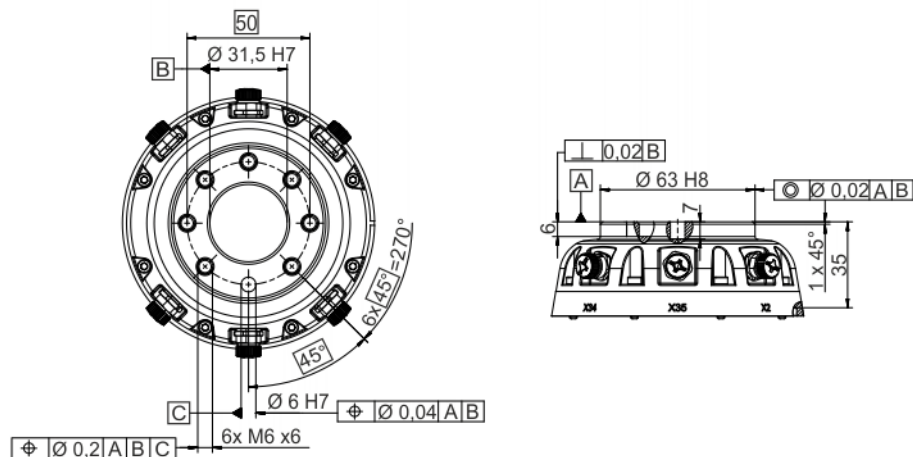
Abmessung, Medien-Flansch elektrisch
